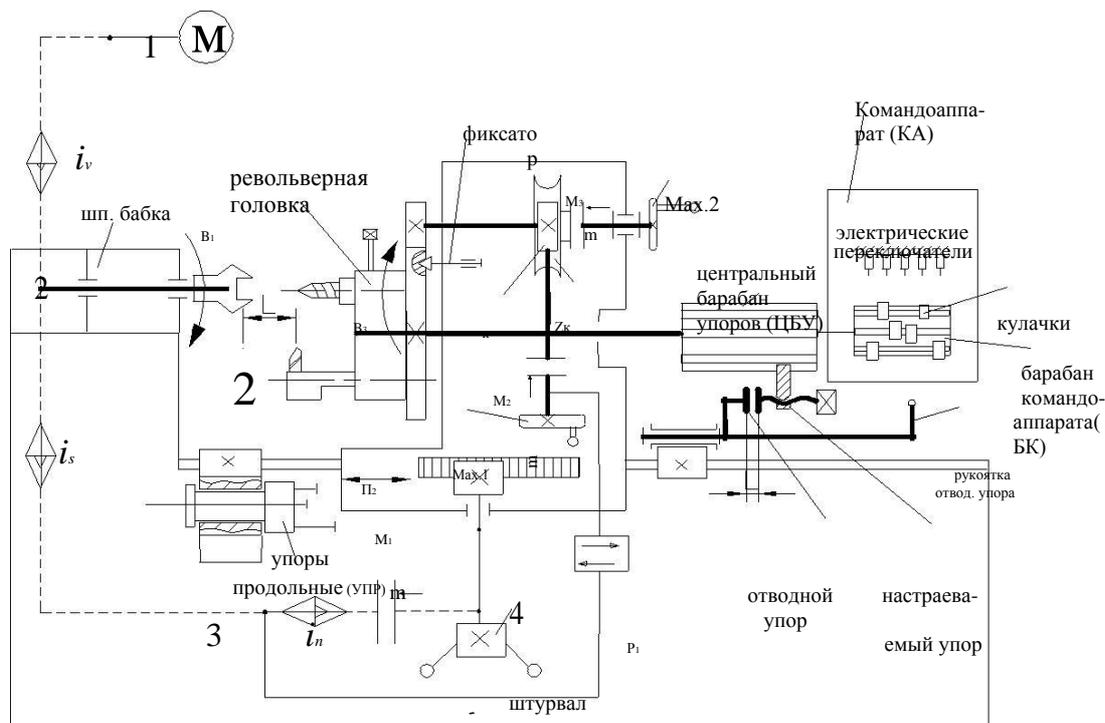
Структурная схема токарно-револьверного станка модели 1341
